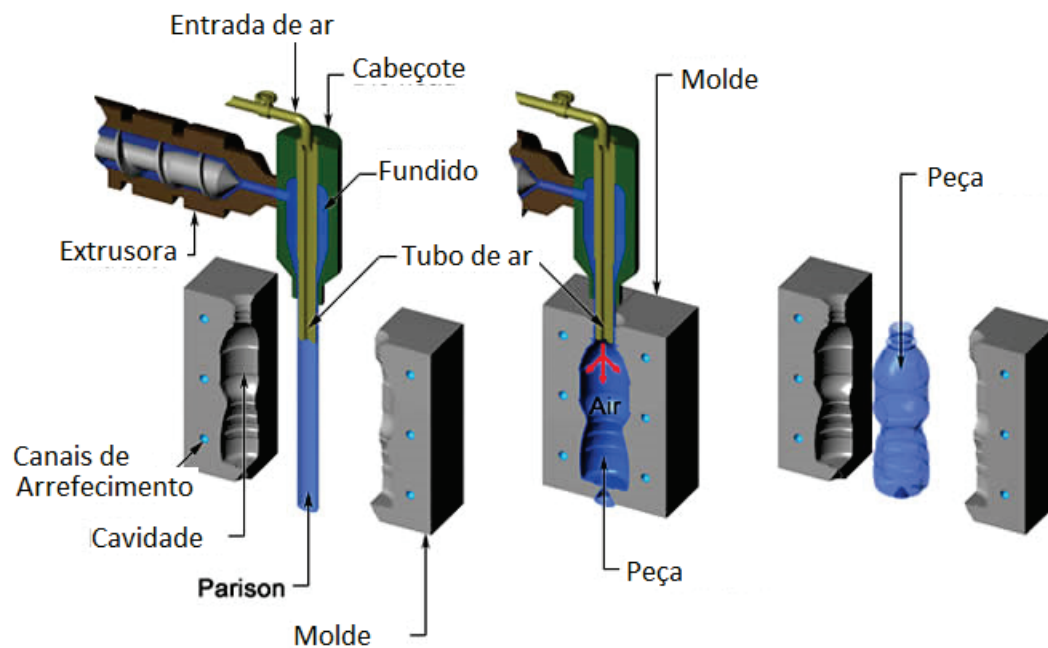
Processo de moldação por sopro (Indústria Hoje).
